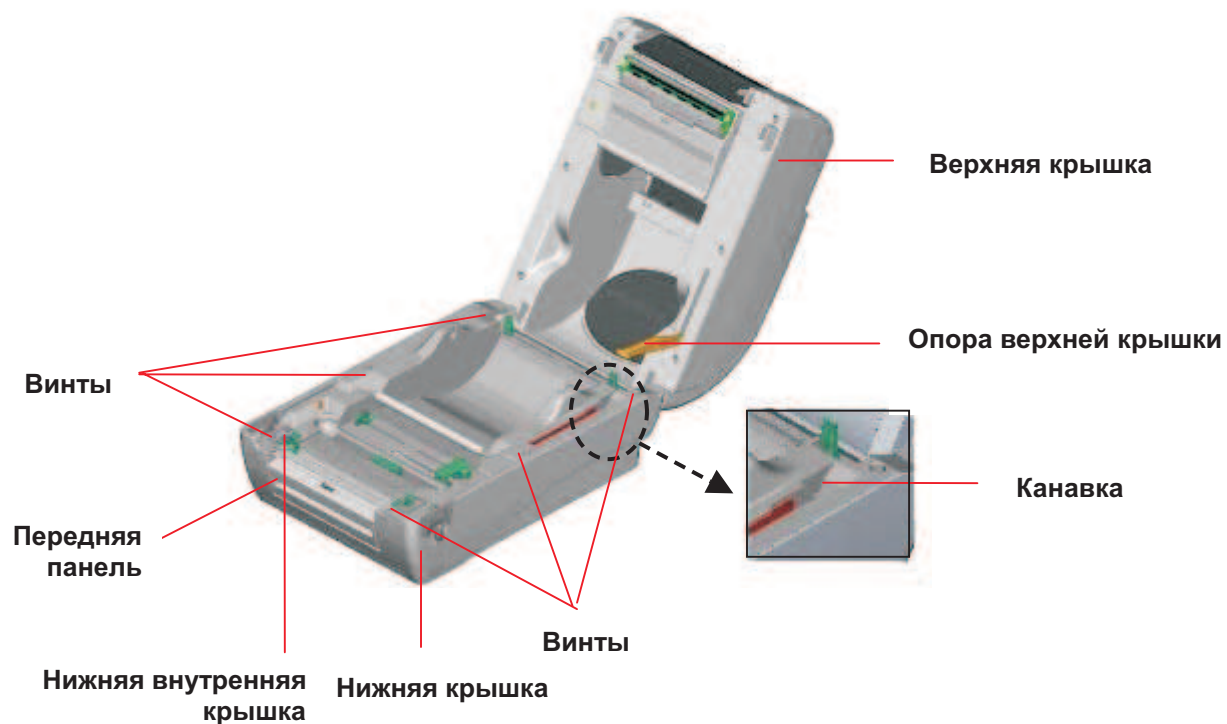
Отверните 6 винтов нижней внутренней крышки
